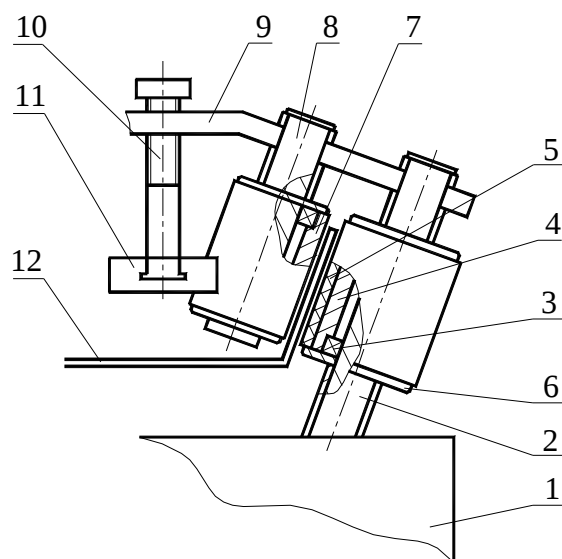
Межклетевая проводка с наклонными валами: 1 – промежуточная клеть, 2 – не приводной вал, 3 – подшипник; 4 – втулка; 5 – полиуретановая втулка; 6 – крышка, 7 – поддерживающая втулка, 8 – дополнительный вал, 9 – серьга, 10 – поджимной винт, 11 – вилка, 12 – профиль
